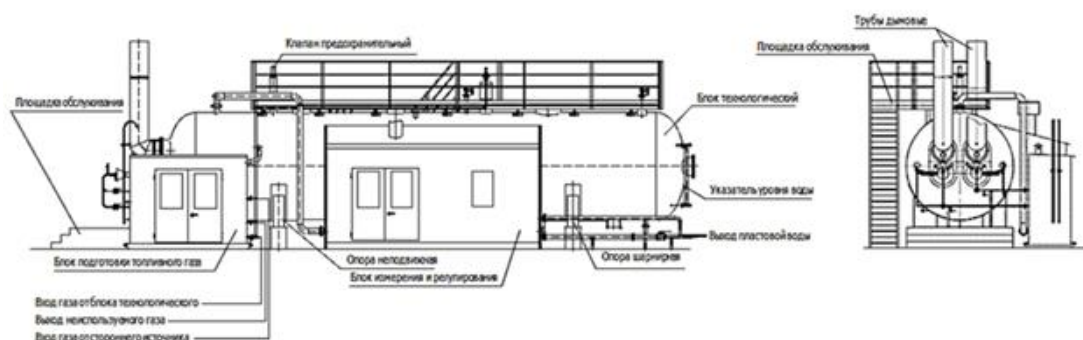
Оборудование установки подготовки нефти УПН
